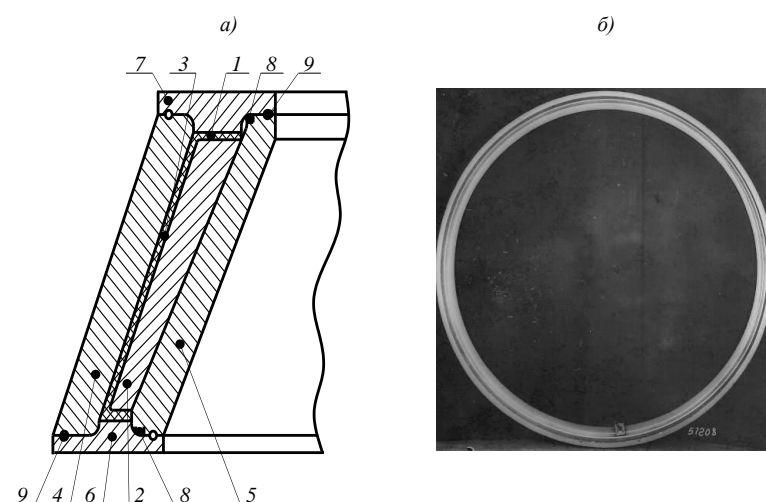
Форма для изготовления колец пропиткой под давлением (а) и готовое изделие (б):
